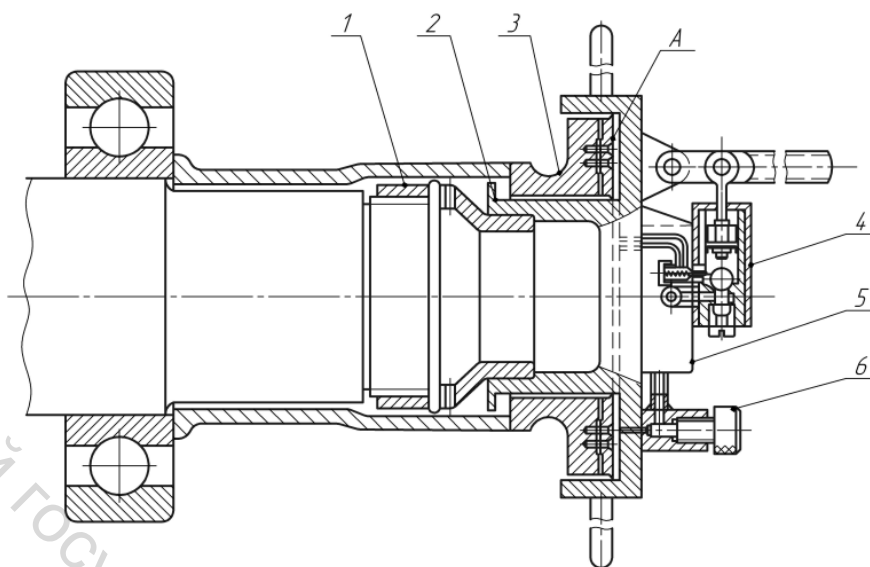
Напрессовка крупногабаритного подшипника качения с помощью гидравлического приспособления
